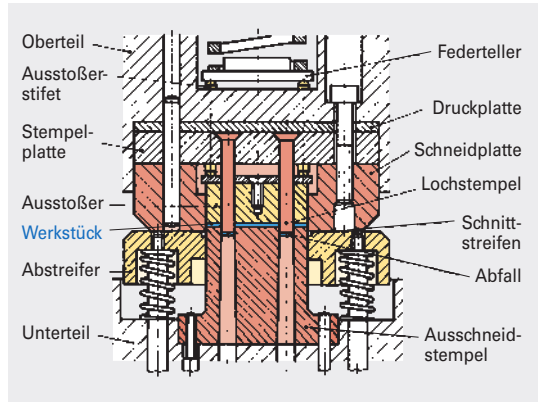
Hauptteile des Gesamtschneidwerkzeuges
